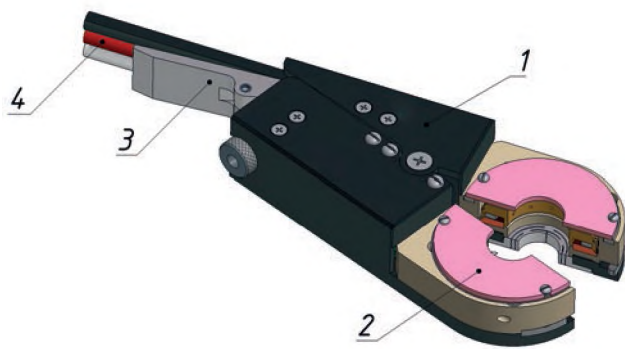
Модель малогабаритной камерной сварочной головки
